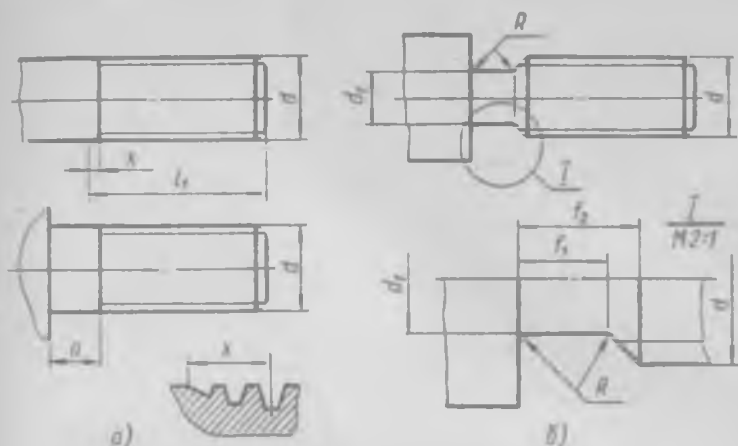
Сбег, недорезы и проточки для наружной метрической резьбы
